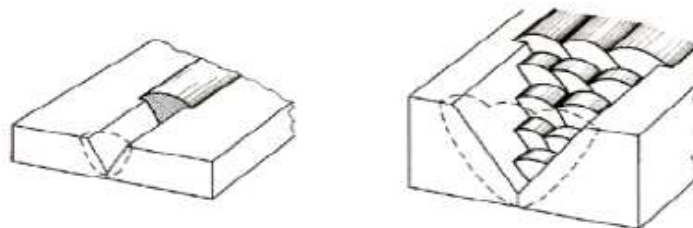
Exemple de soudage monopasse (gauche) et multipasse (droite)
